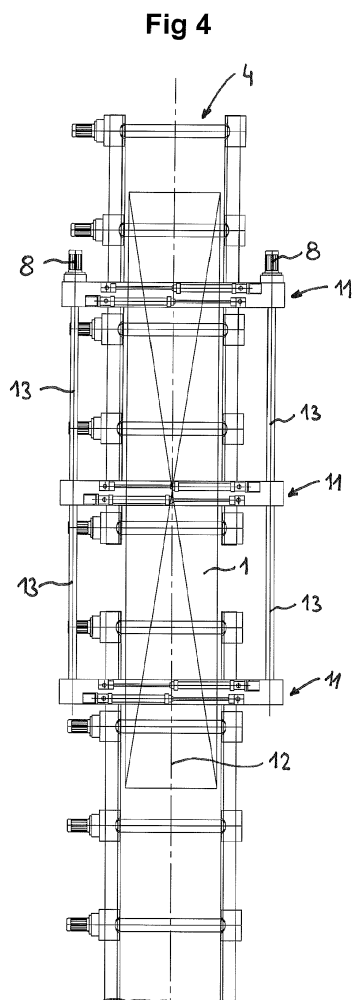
Grundriss des Kettenbrammenwenders aus Abbildung 16<sup>29</sup>
